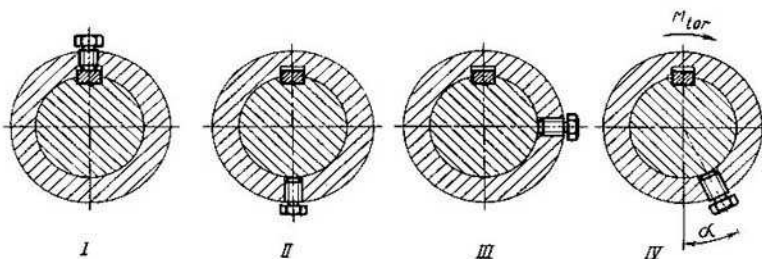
Procedimientos para colocar los tornillos de presión en un árbol con chaveta
